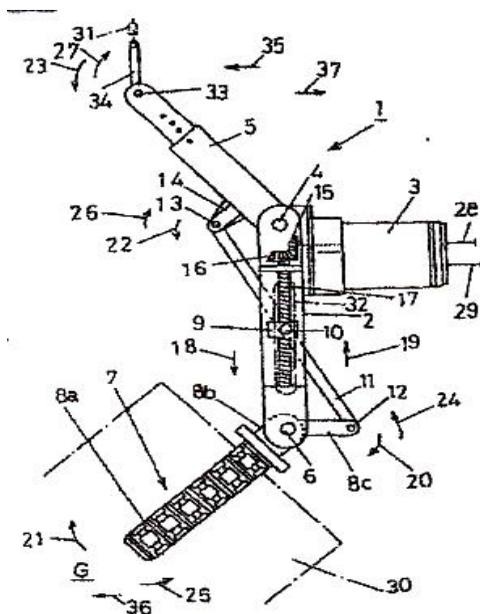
Внутренний захват, дополнительно оснащенный манипулирующими приспособлениями
